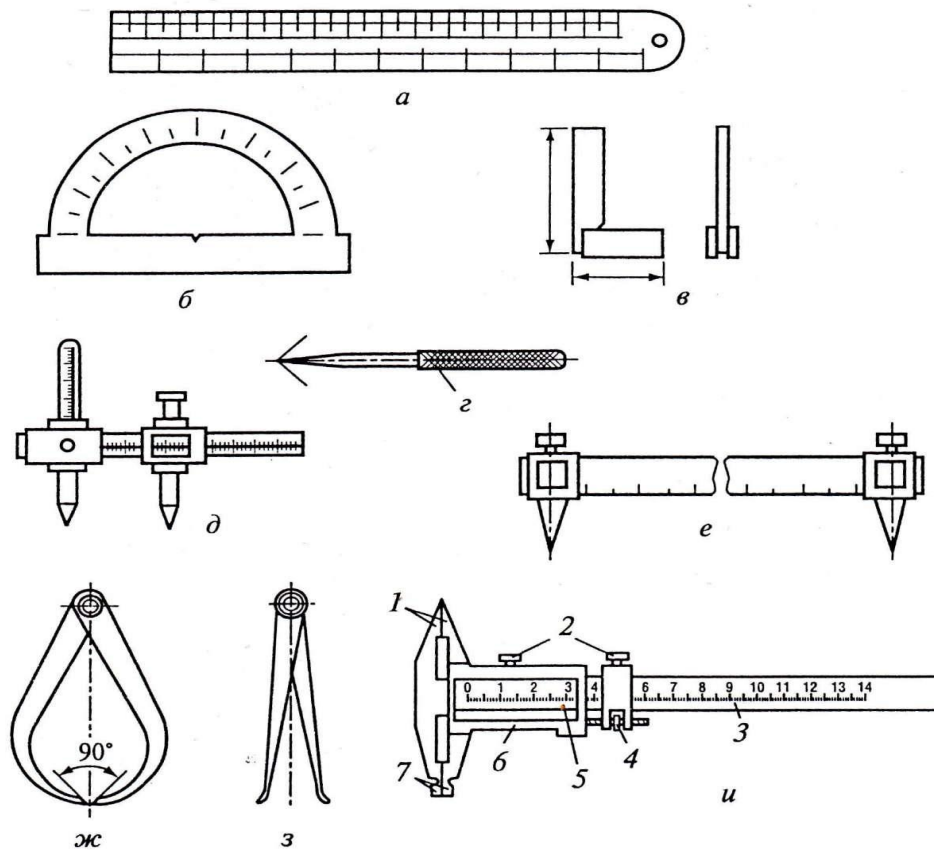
Розмічувальний інструмент: *а* – лінійка вимірювальна металева, *б* – транспорир; *в* – косинець слюсарний; *г* – керн; *д* – циркуль; *е* – рейсмус жерстяний розсувний; *ж* – кронциркуль нормальний; *з* – нутромір; *и* – штангенциркуль; 1 – нерухома і рухома губки для зовнішнього вимірювання; 2 – стопорні гвинти; 3 – штанга з міліметровими поділками; 4 – гвинт ноніуса; 5 – ноніус; 6 – пересувна рамка; 7 – нерухома і рухома губки для внутрішнього вимірювання
